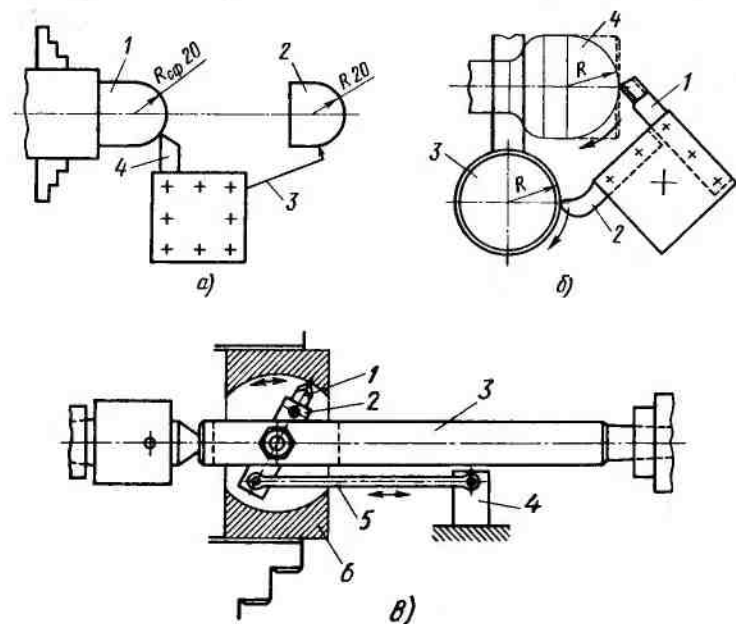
Приспособления для обработки сферических поверхностей:
